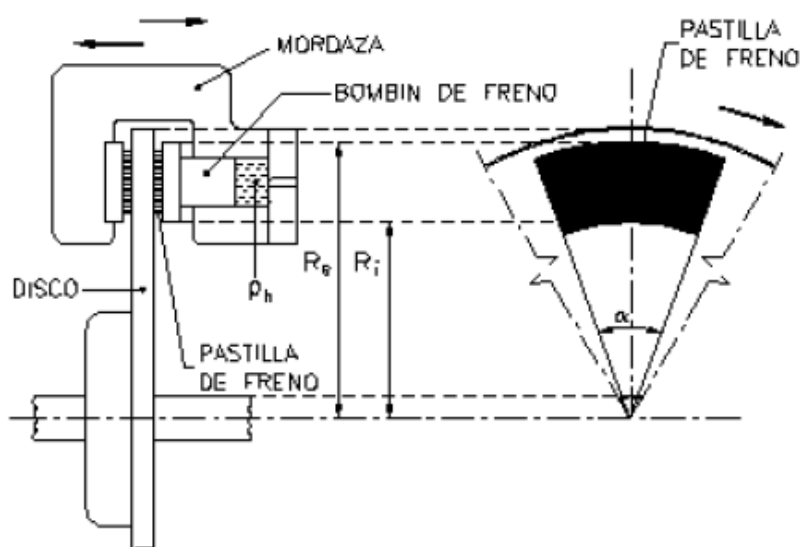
PARTES DEL FRENO DE DISCO Y PASTILLA
